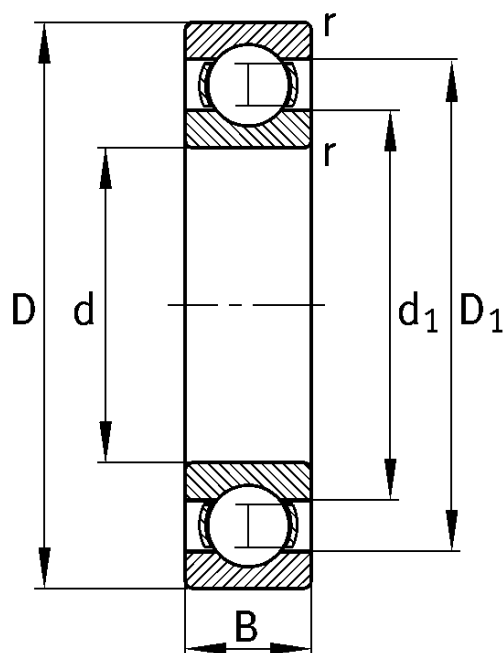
Габаритные размеры серии 16005 ф. INA
